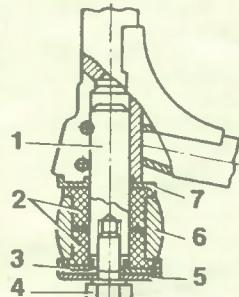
Левый узел крепления задней вилки (рычага): 1 — левая цапфа; 2 — резиновые втулки; 3 и 7 — зажимные шайбы; 4 — стяжной болт; 5 — защитный стакан; 6 — ухо вилки.
